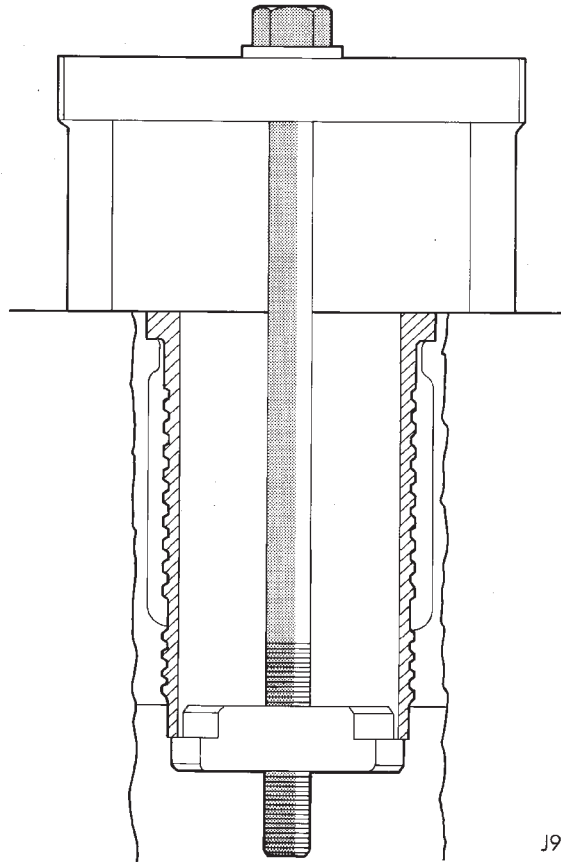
Ausbauwerkzeug für Laufbuchsen
